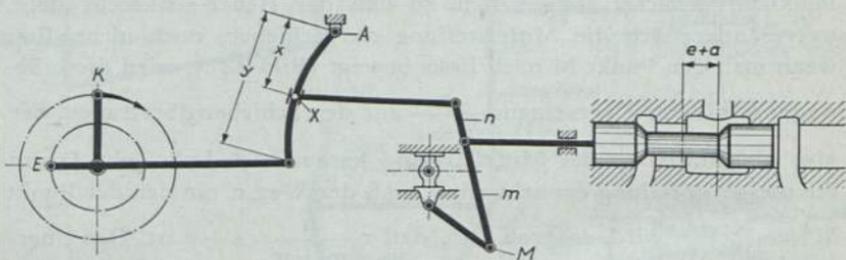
Wirkungsweise der Heusinger-Steuerung (Mittellage des Kolbens)
